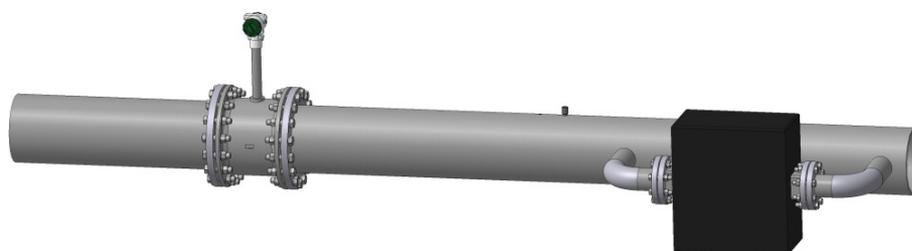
Монтаж ТЭГ на трубопровод
